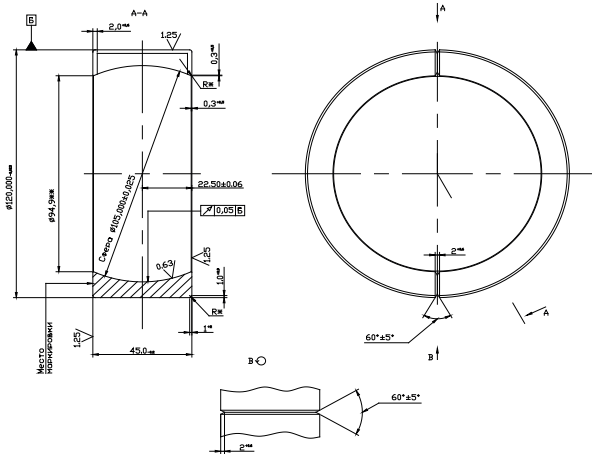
Наружное кольцо шарнирного подшипника типа ШСЛ-70 (MIZ)
